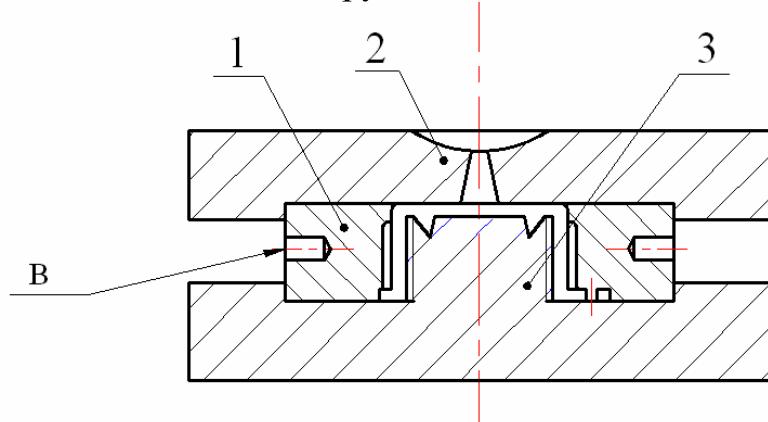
Прес-форма для виготовлення пластмасових заглушок
